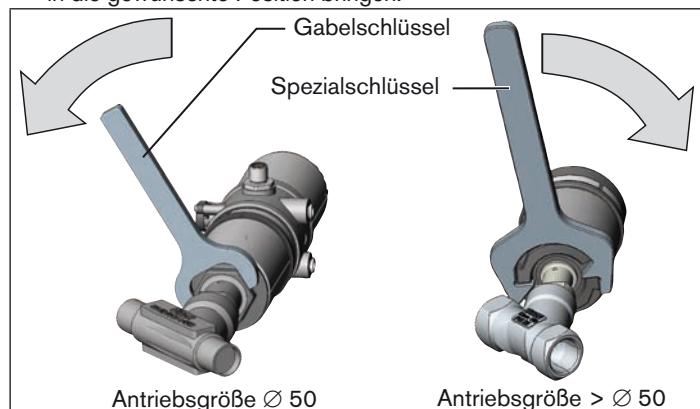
Drehen mit Gabelschlüssel / Spezialschlüssel
